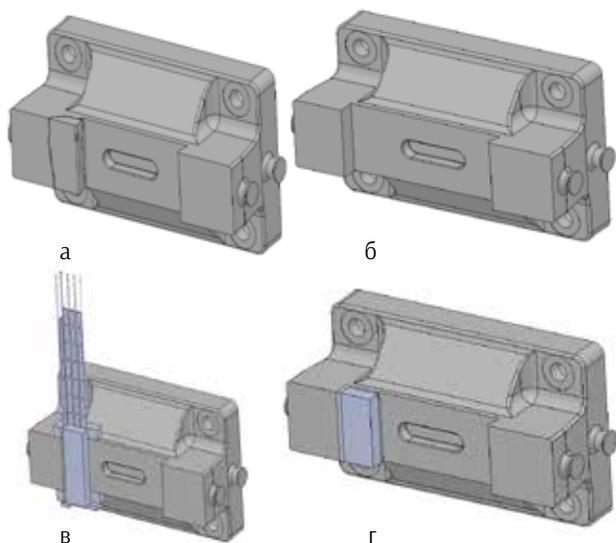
Ремонт захвата «ласточкин хвост» детали «Корпус», разрушенного трещиной: а – корпус с отколотой частью рабочей поверхности, б – выборка механической обработки пораженного трещиной участка, в – сборка под ЭШС заготовки со вставкой, г – после ЭШС и отрезки технологических планок
